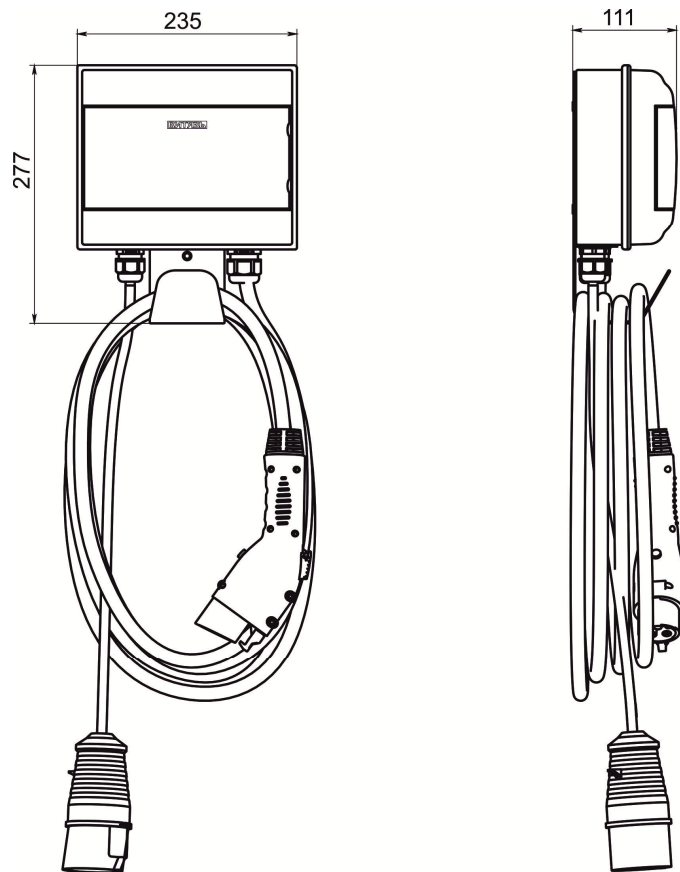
Габаритный чертеж станций EC-302-11, EC-302-31, EC-302-71
